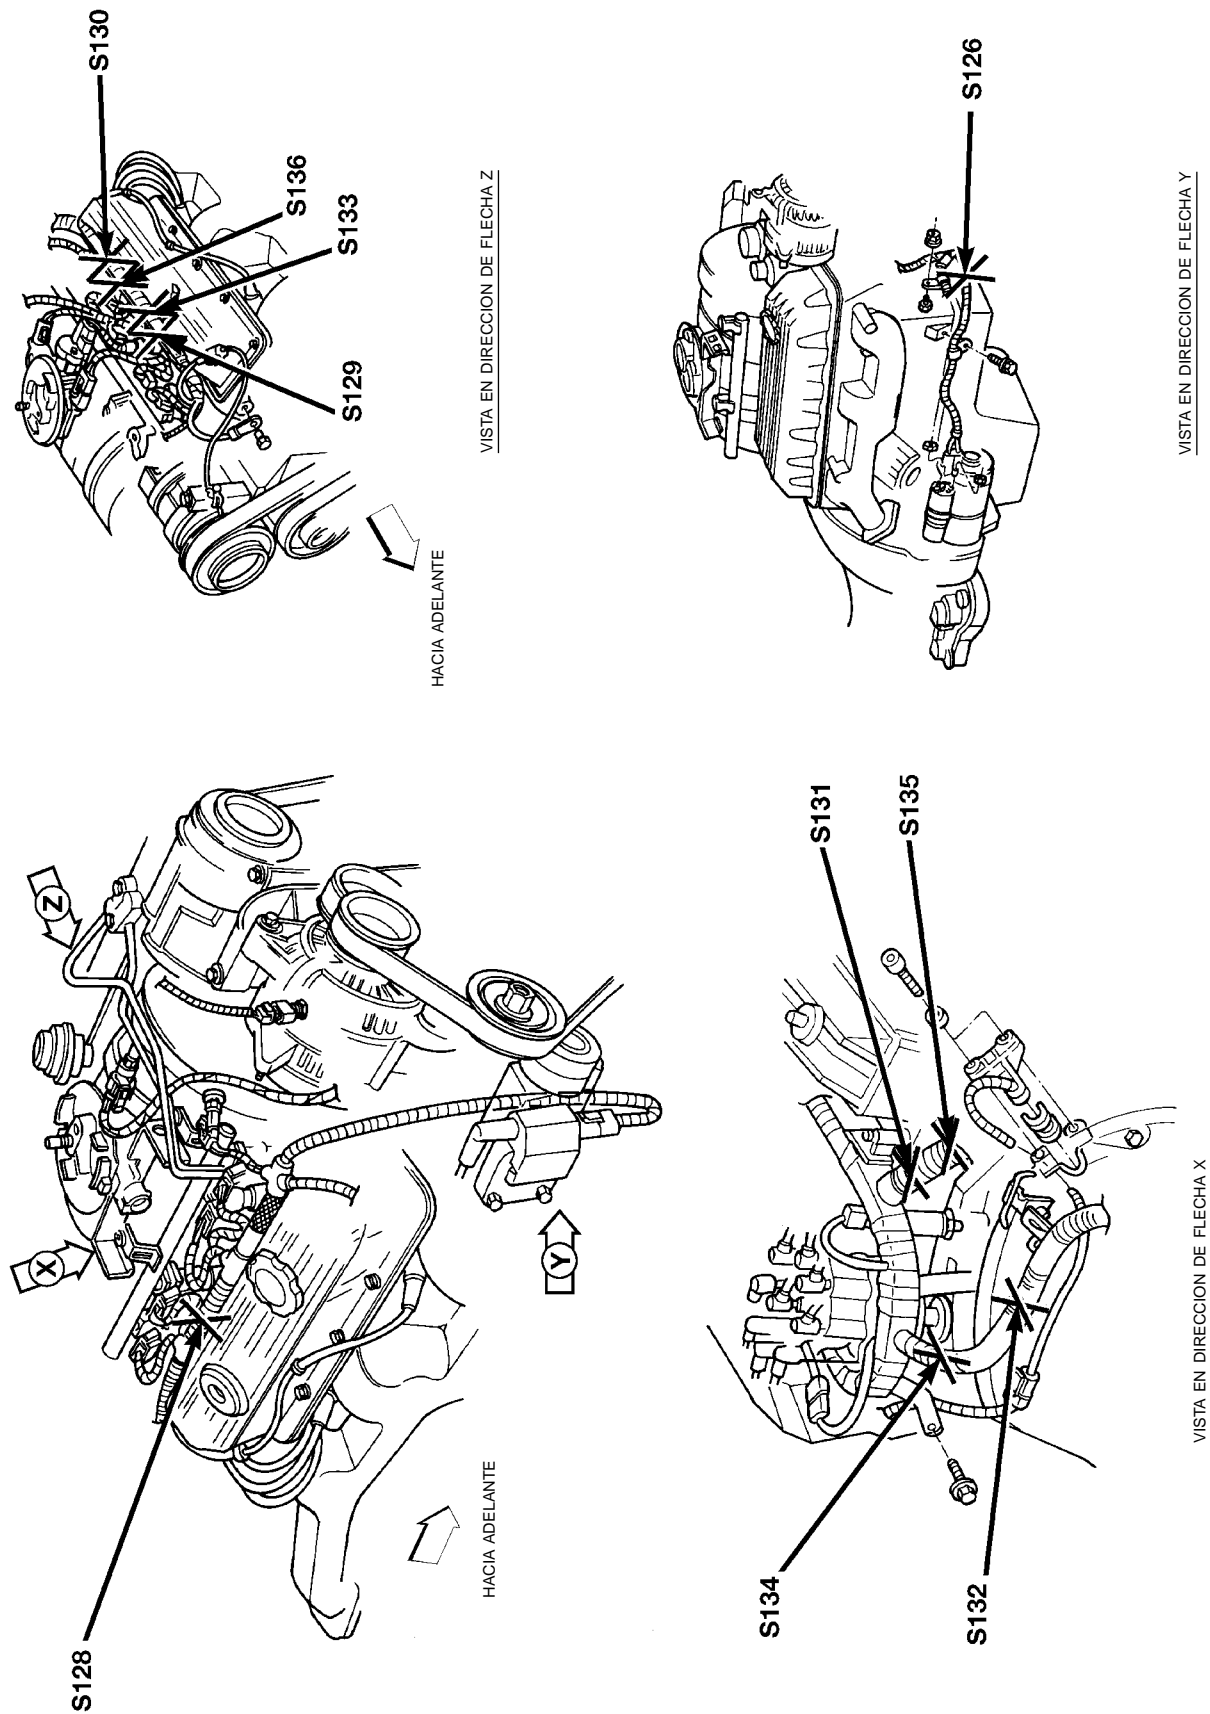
Empalmes del cableado del motor—Motor 5.2L
